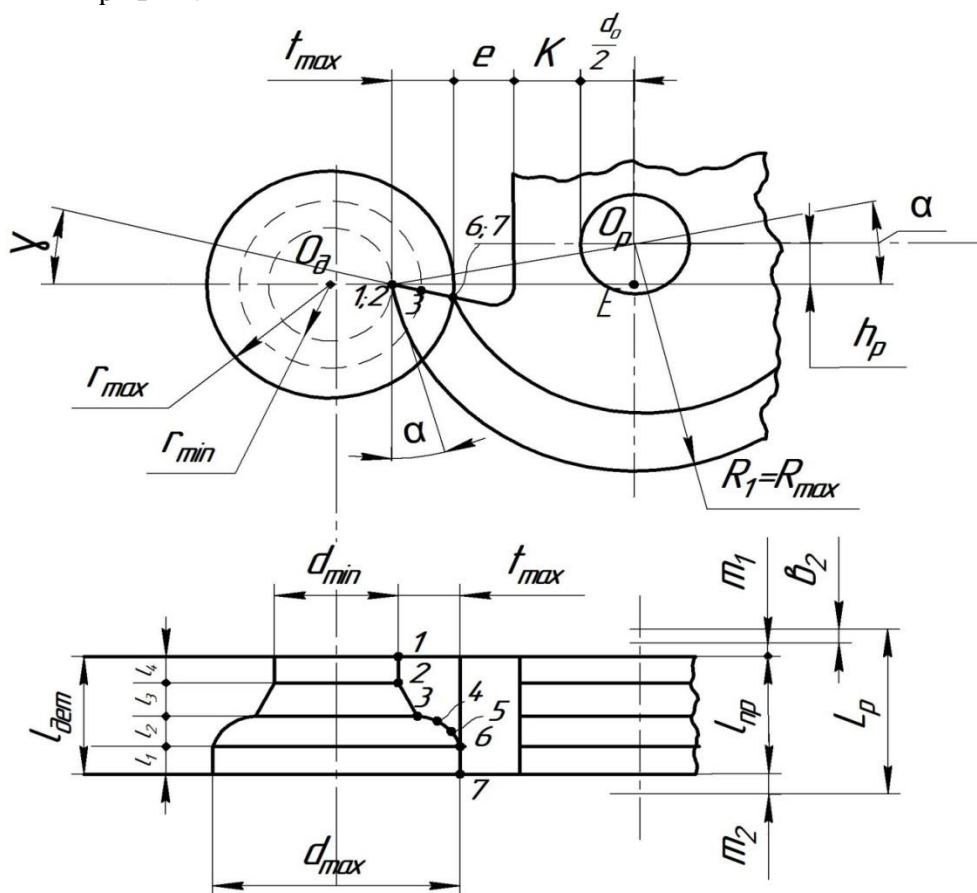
Схема к определению габаритных и присоединительных размеров фасонного резца
